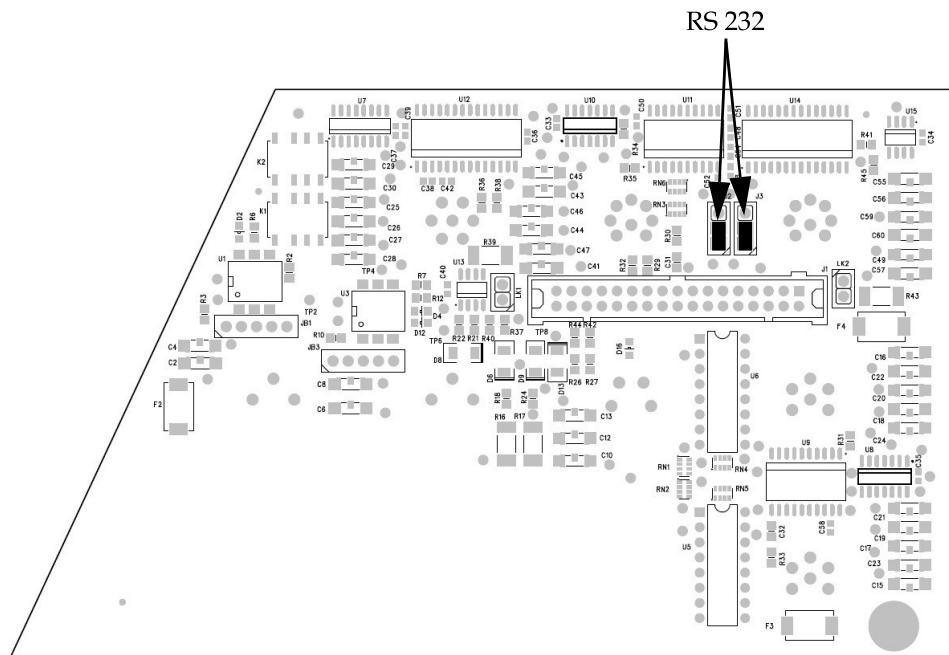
Configurações do jumper RS 232 (PCB 7)
